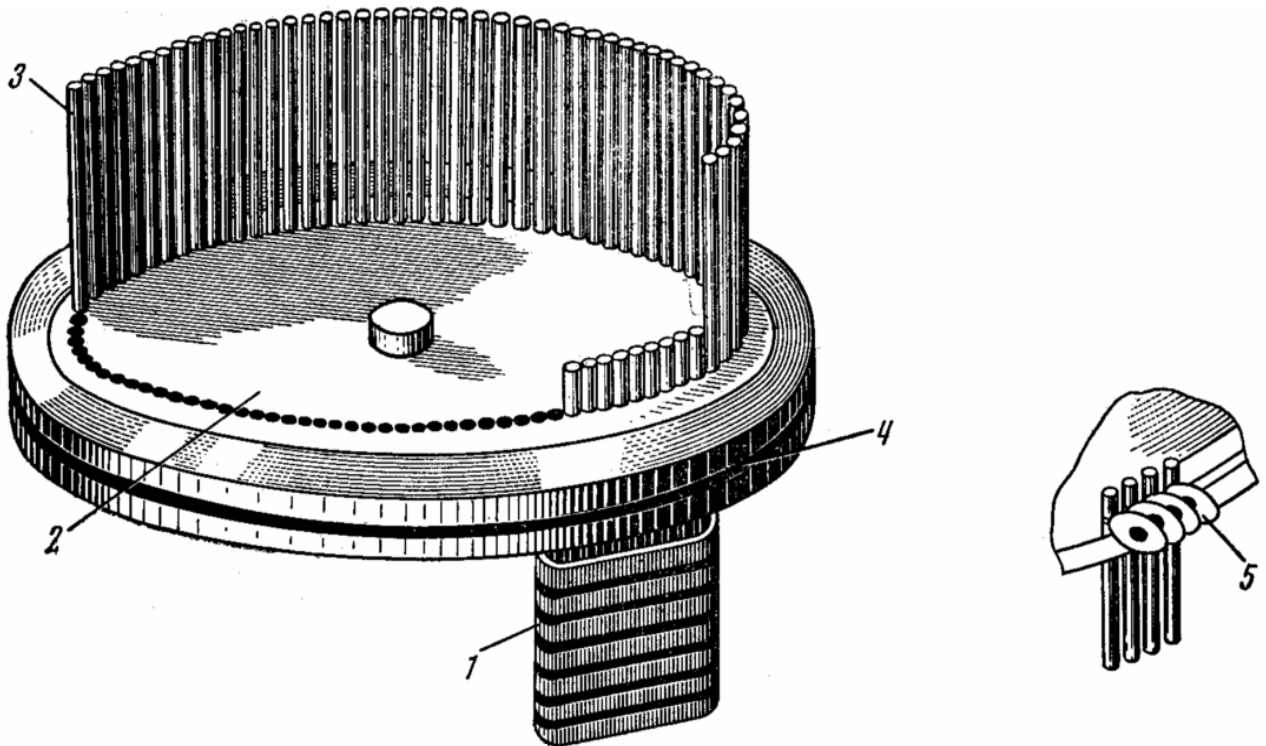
Кинематическая схема индукционного нагревателя для концов мерных заготовок: 1 – овалный индуктор; 2 – диск; 3 – заготовки; 4 –ограничительное кольцо; 5 – замки
